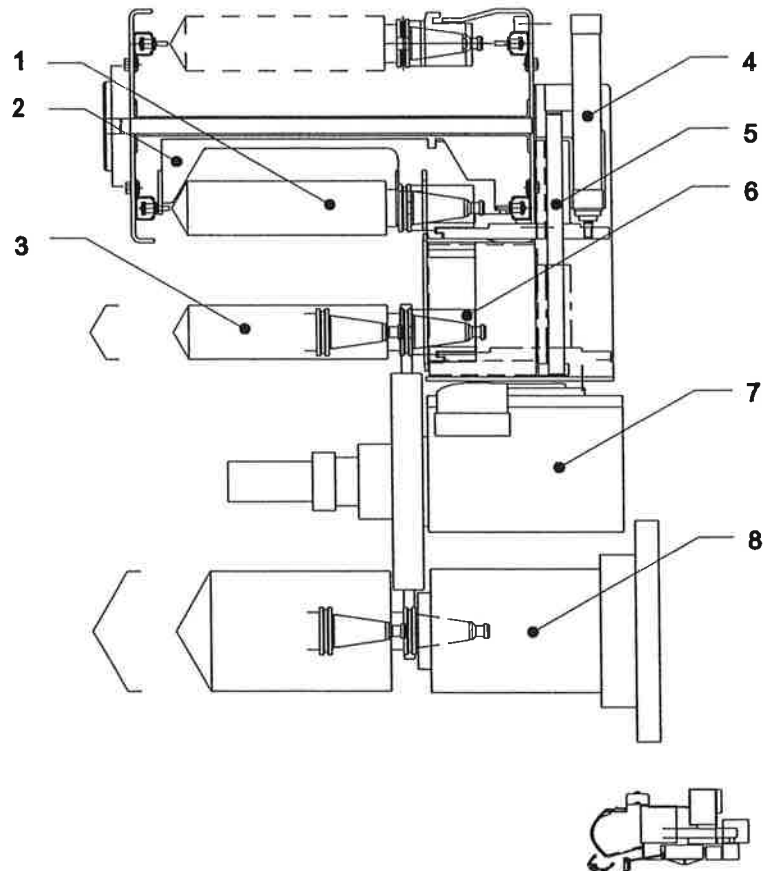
Verschiebeeinrichtung mit Werkzeugmagazin und Werkzeugwechsler, Draufsicht
